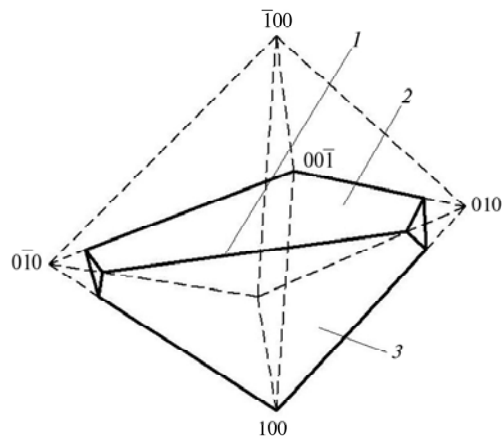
Схема ориентации режущих кромок резца в форме октаэдра: 1 – режущая кромка; 2 – передняя поверхность; 3 – задняя поверхность.
